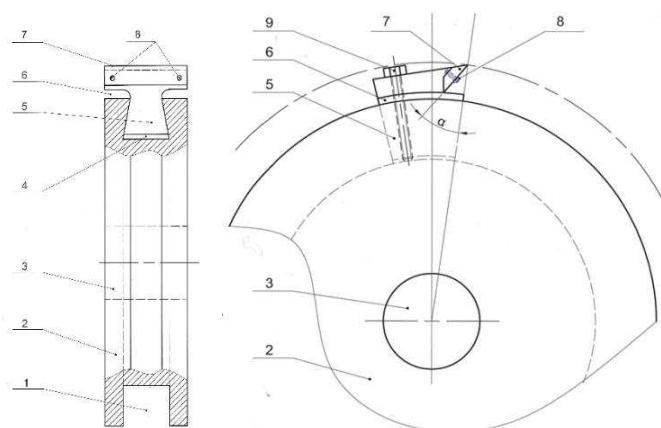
Конструкция фрезы с регулируемым числом режущих элементов (вариант 2)
